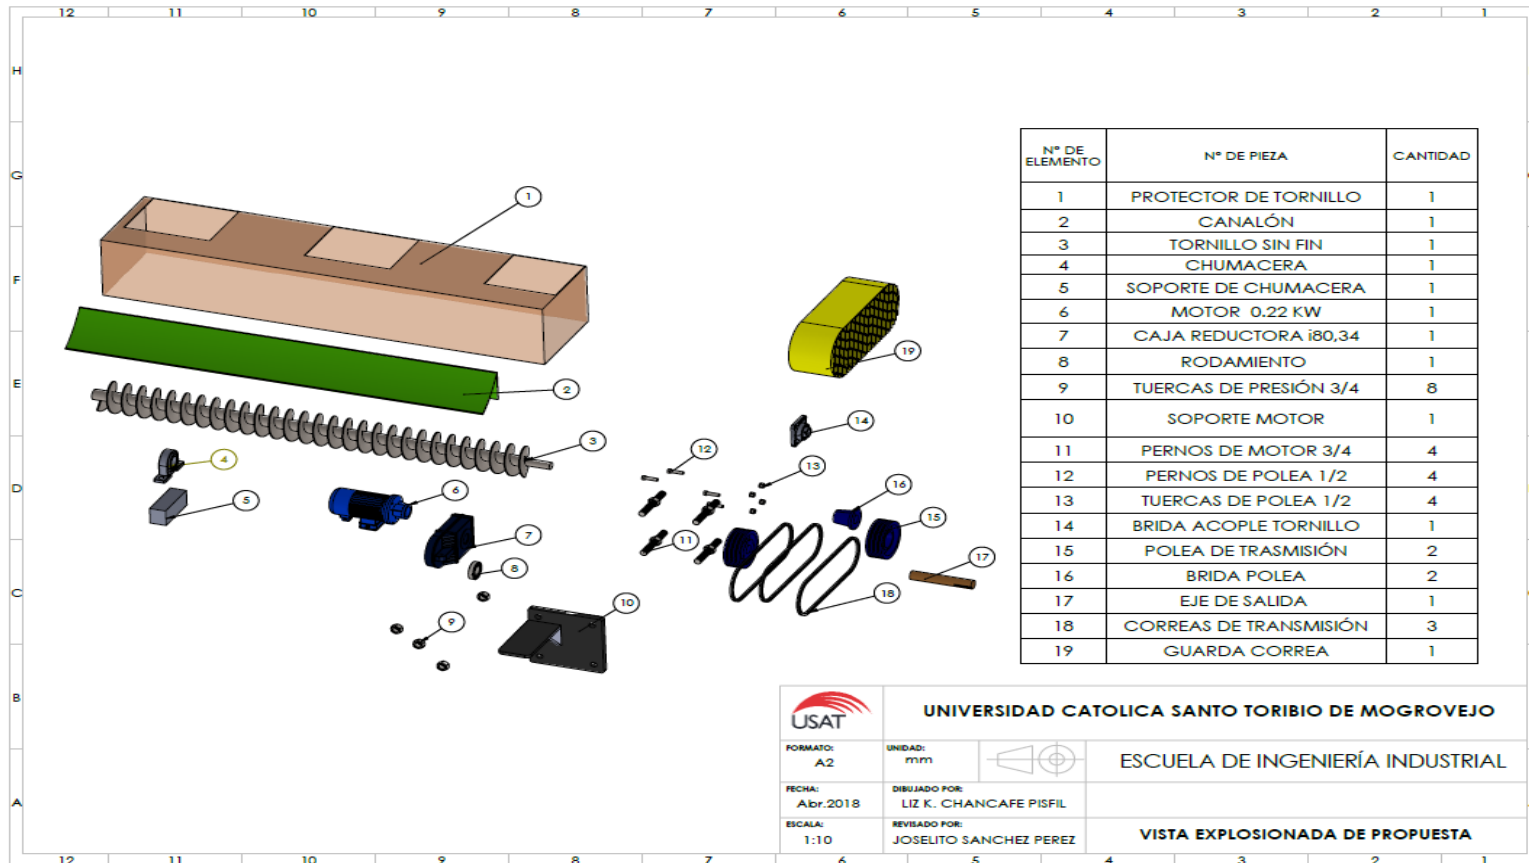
Partes del Diseño del tornillo sinfín especial propuesto
